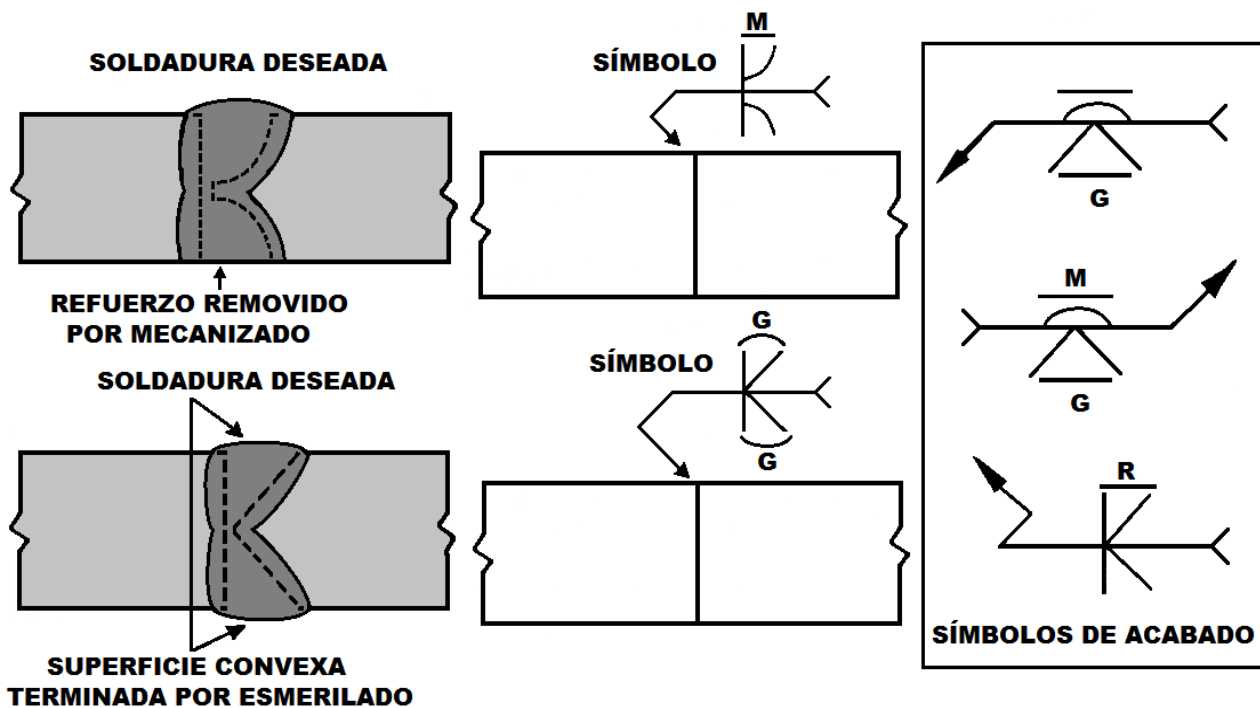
Acabado en los cordones de soldadura (8, 18, 31)
